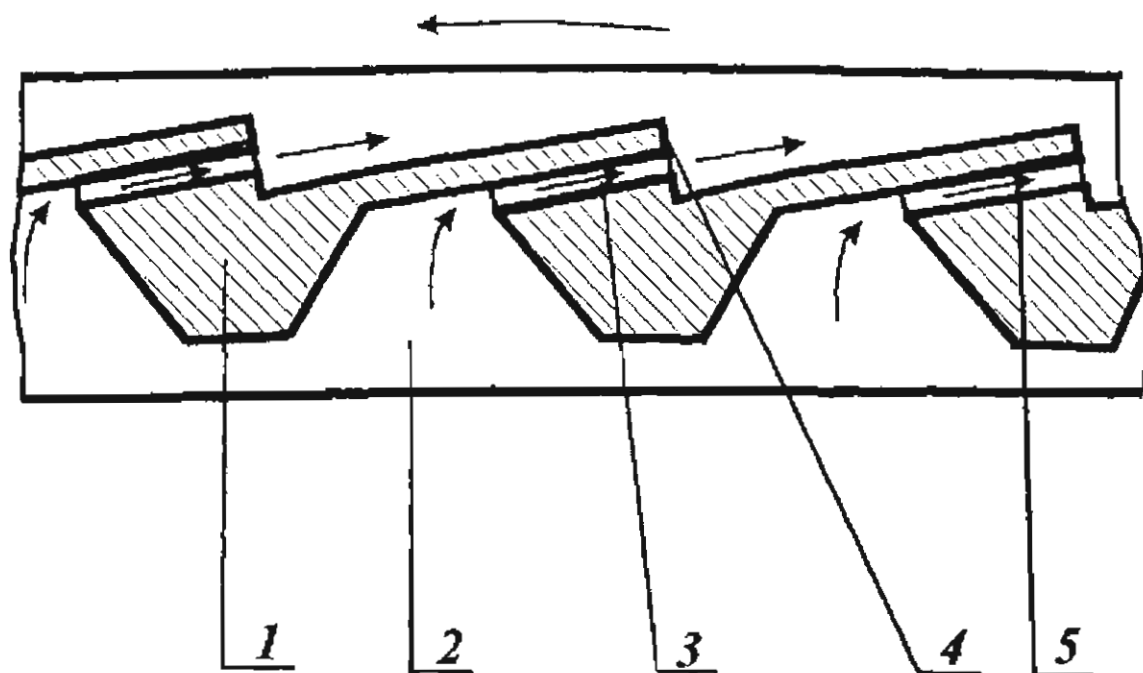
Возможная конструкция обечайки ротора щелевого детандера
